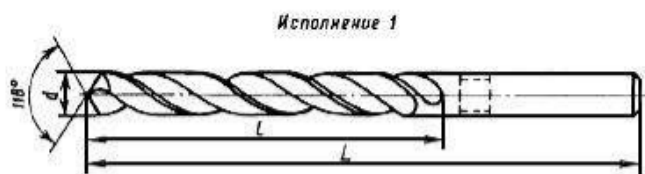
Сверло 2300-0226 ГОСТ 10902-77
